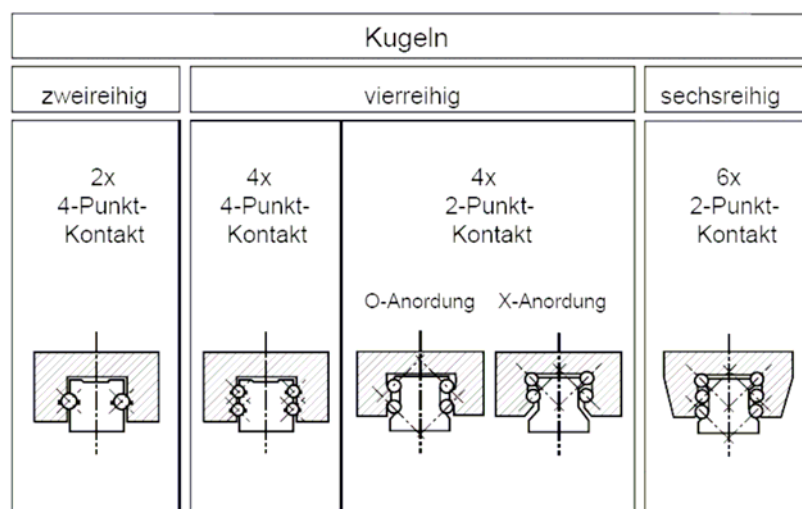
Bauformen von Profiwälzführungen mit Kugeln [3]
